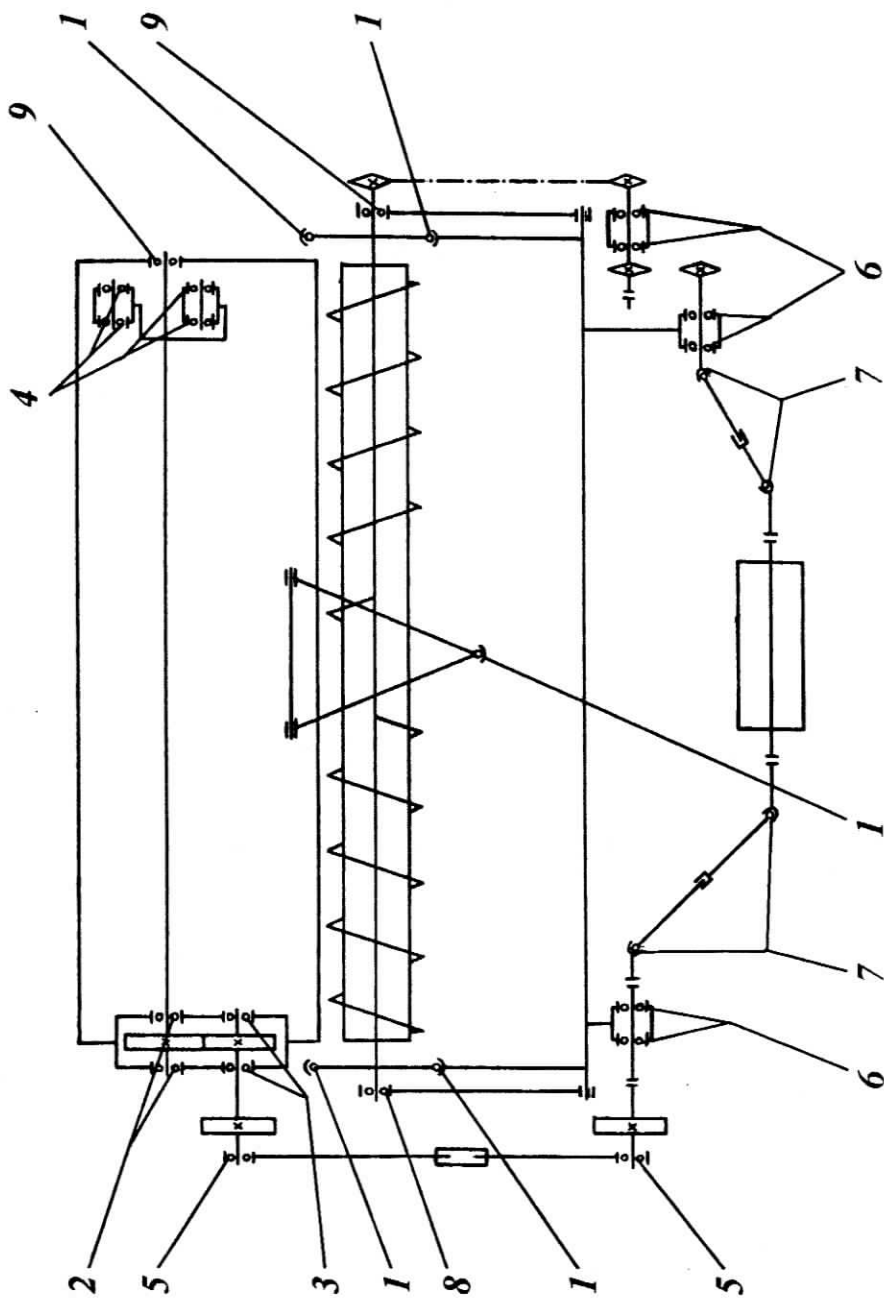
Схема расположения подшипников платформы-подборщика РСМ-100.72 к комбайну "Дон-680".
